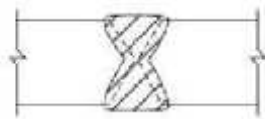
Soldadura a tope doblemente soldada¹¹
